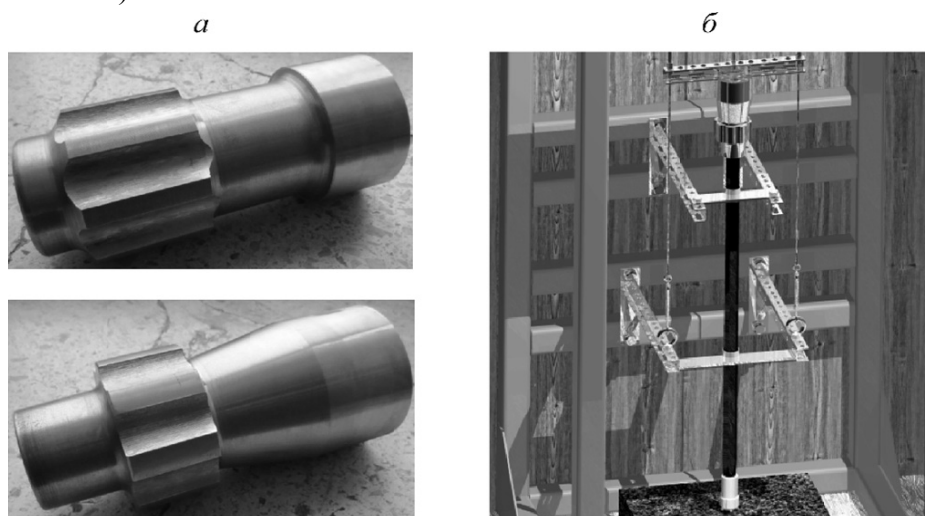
Опытные образцы бойков пневмоударника ПП110ЭН (*а*) и экспериментальный стенд (*б*)
